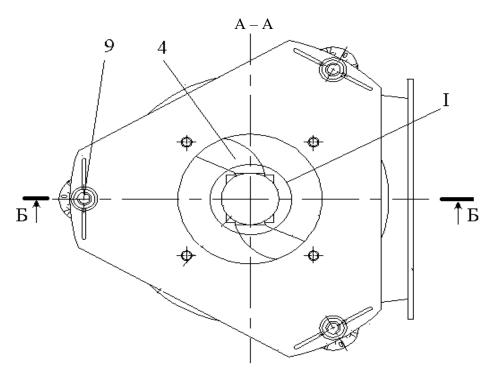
Схема измельчителя (вид A-A): 1 — Полость камеры измельчения первой ступени; 4 — нож; 9 — регулировочный винт
